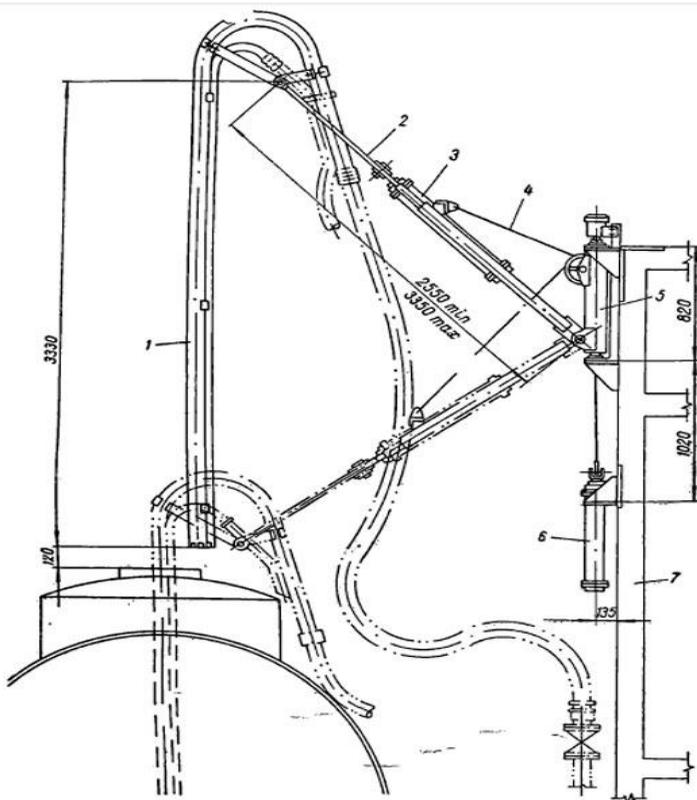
Укосина раздвижная с гидроприводом для подачи наливного рукава в вагон-цистерну: 1 – наливной рукав; 2 – укосина; 3 – гидроцилиндр выдвигения укосины; 4 – трос; 5 – гидроцилиндр поворота; 6 – гидроцилиндр подъема; 7 – стойка эстакады.
